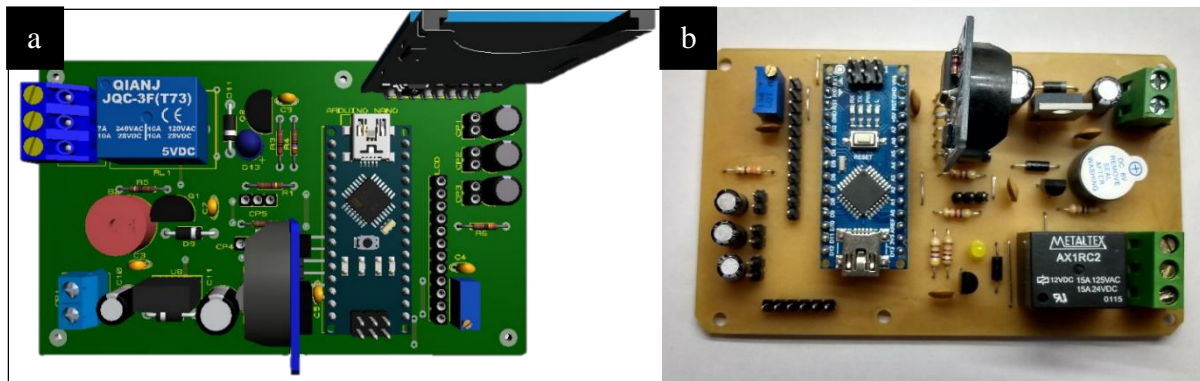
Hardware do Datalogger, sendo (a) Layout da PCB em 3D e (b) a PCB física
